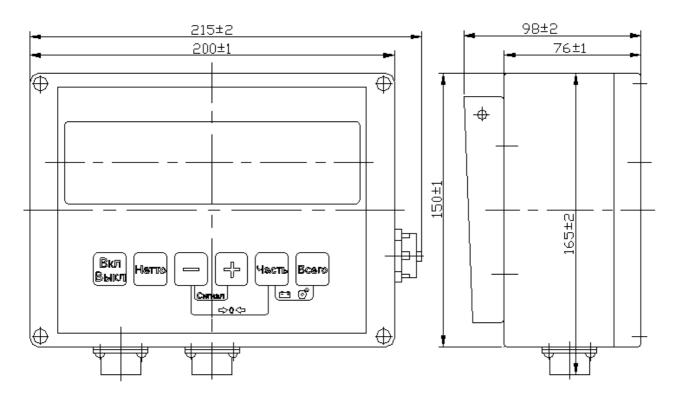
Габаритные, установочные и присоединительные размеры БИУ.02
